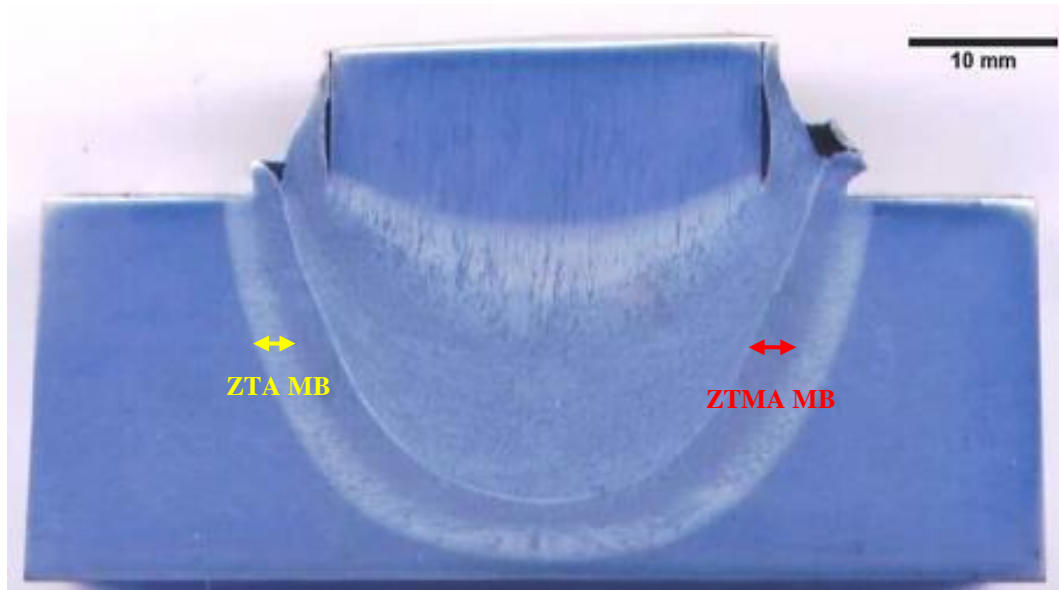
Macrografia da solda F60 na condição de como soldado. Ataque Nital 2%.
